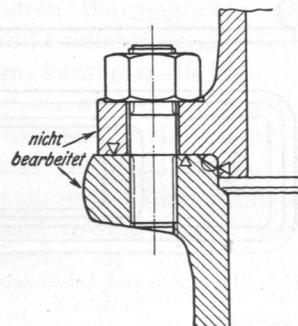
Einschränkung der Bearbeitung durch geeignete Formgebung.
